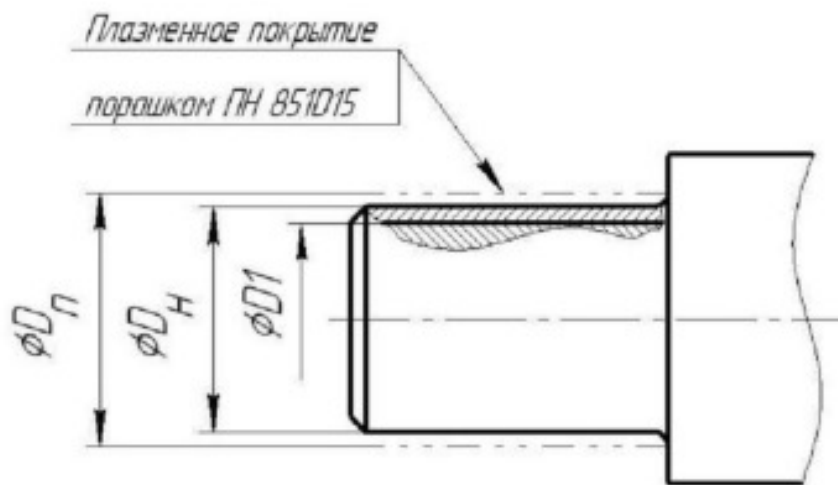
Оформление нанесения восстанавливающего покрытия на изнашиваемую поверхность
